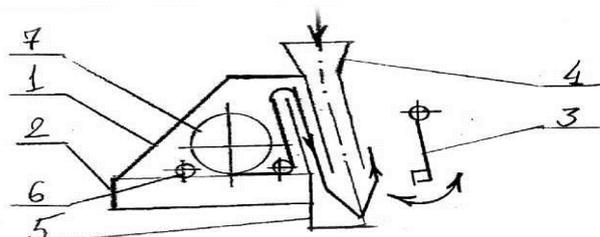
Технологическая схема устройства для упаковки: 1-корпус 2-панель управления 3 - узел термосварки 4 - приемный бункер 5 - ограничительный столик 6 – ленто-протяжная система 7- рулон с плёнкой
